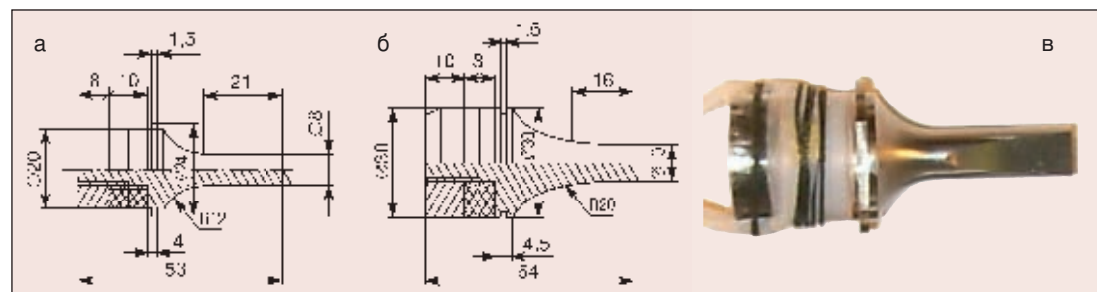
Полуволновая пьезоэлектрическая УЗКС для сварки термопластичных материалов: а — ручной вариант; б — стационарный вариант; в — внешний вид
